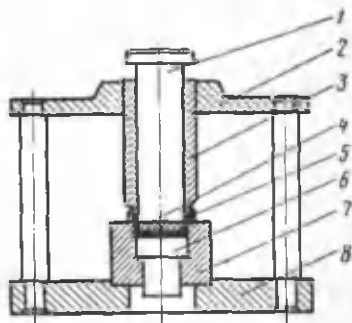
Прессформа для запрессовки активной массы в корпус ртутно-цинкового элемента:
